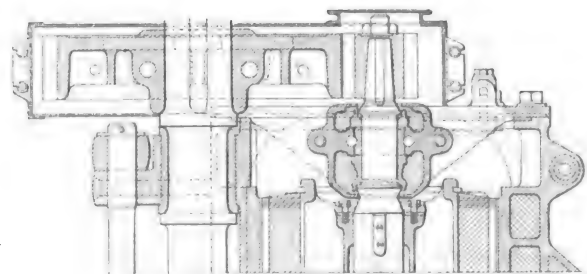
Moteur de tramway de 20 chevaux. Coupe horizontale partielle, côté des engrenages.
